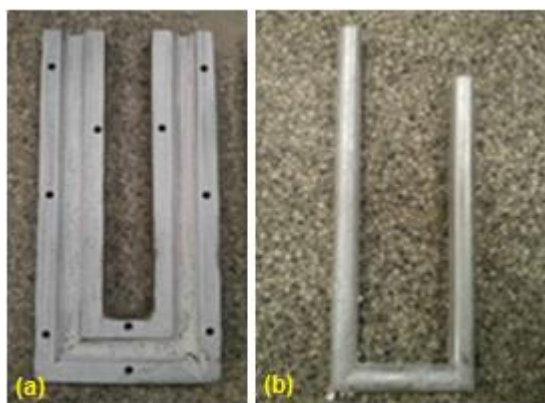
Processo de solidificação: (a) molde metálico em U; (b) amostra após desmoldagem. Fonte: Sousa, 2015.
